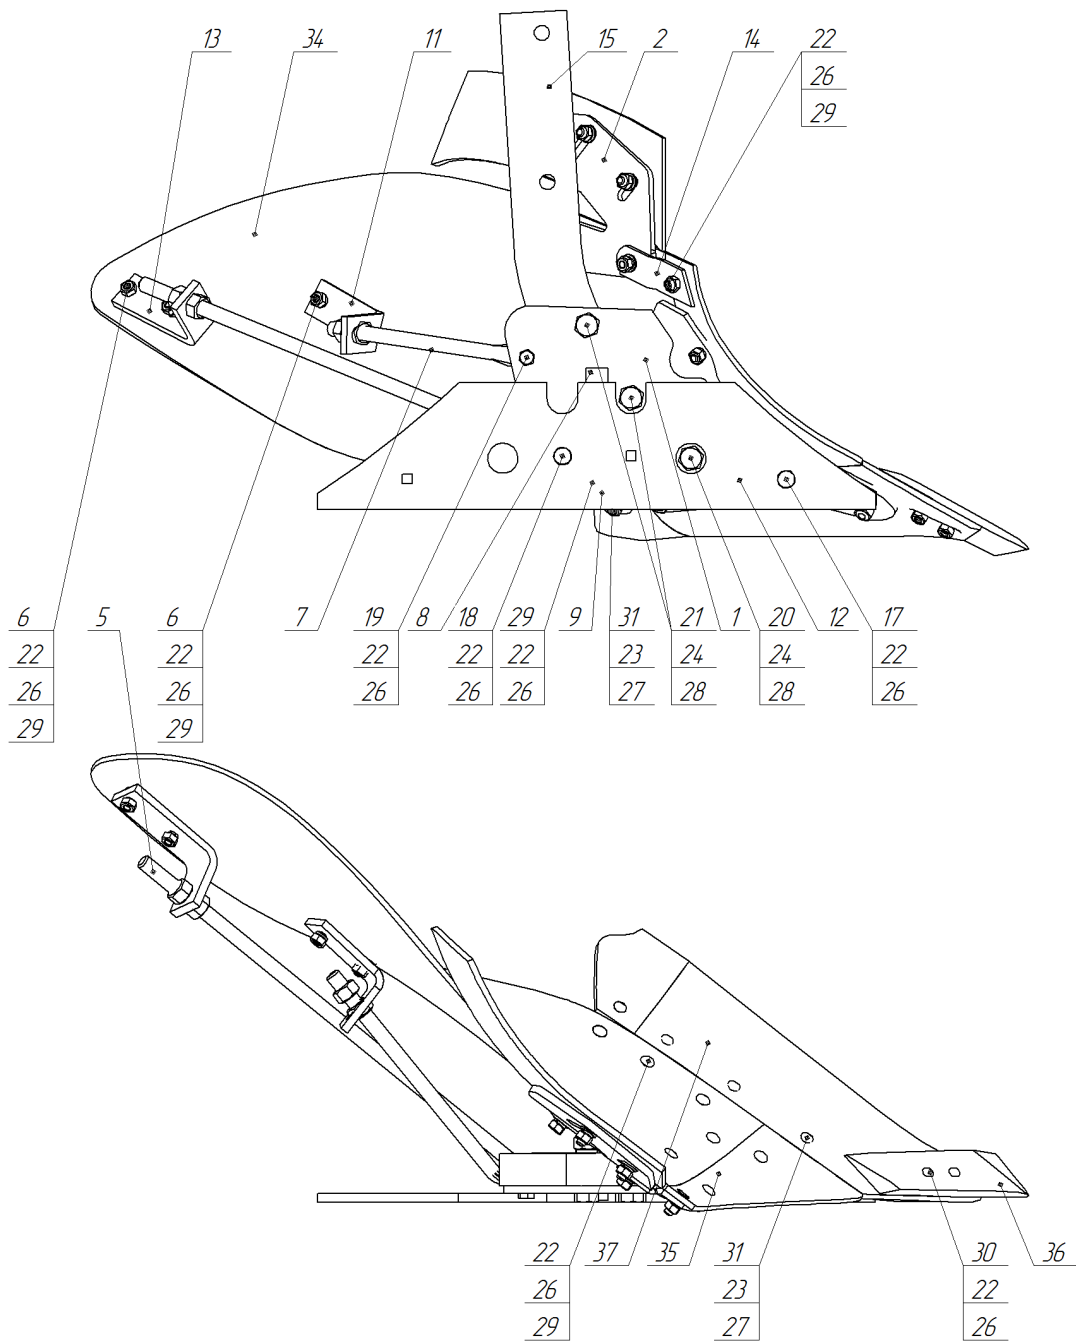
КСО-45 00.00.000-01 Корпус в сборе левый
